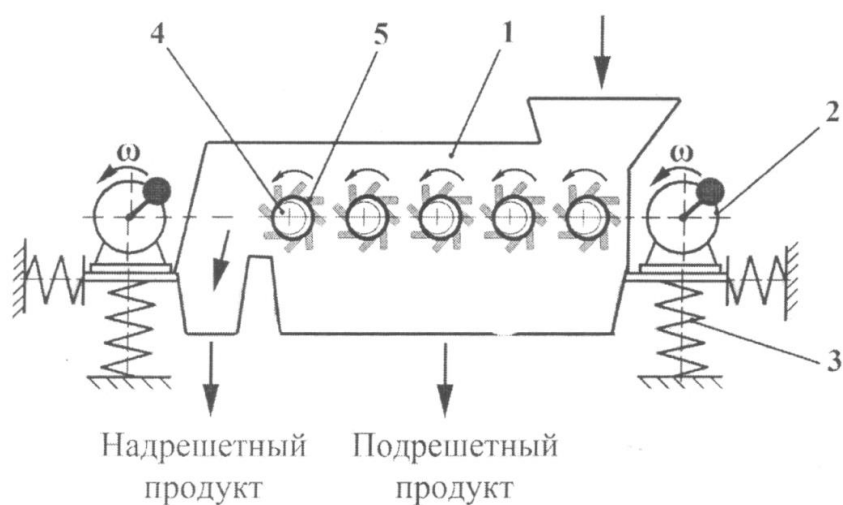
Общий вид конструкции валкового виброударного классификатора: 1 - короб; 2 - инерционный вибровозбудитель; 3 - упругие связи; 4 - эксцентриситет валков; 5 - рабочие валки
